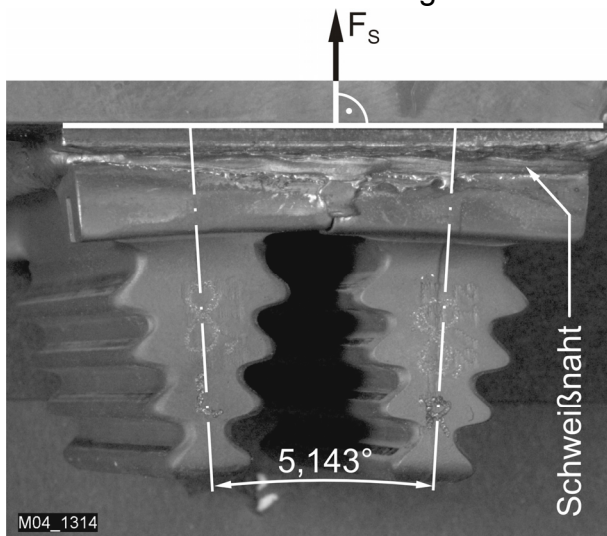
Querschliff durch die Schweißnaht der Elektronenstrahl-Probeschweißung zwischen Schaufelfuß aus IN792 und Krafteinleitung aus IN706
